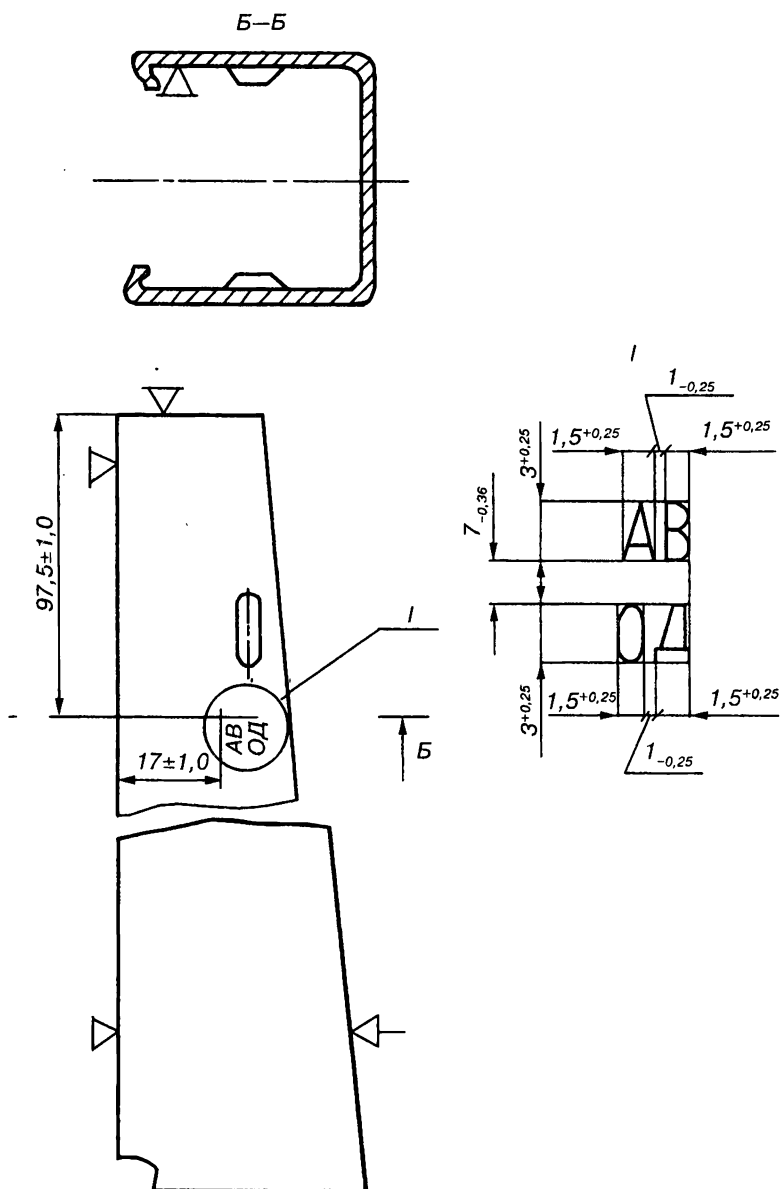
Накатка буквенных знаков на горизонтально-фрезерном станке ВТ80
